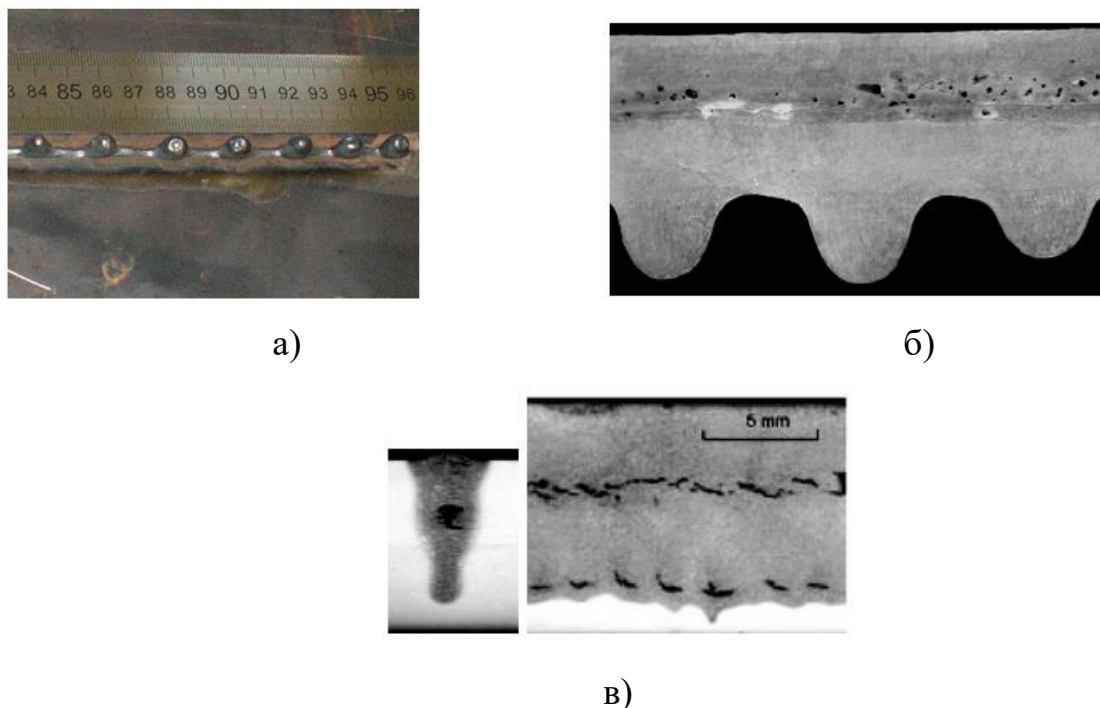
Дефекты сварочных швов, выполненных гибридной лазерно-дуговой сваркой [98]: а) нестабильное формирование обратного валика сварочного шва; б) пористость; в) горячие трещины
